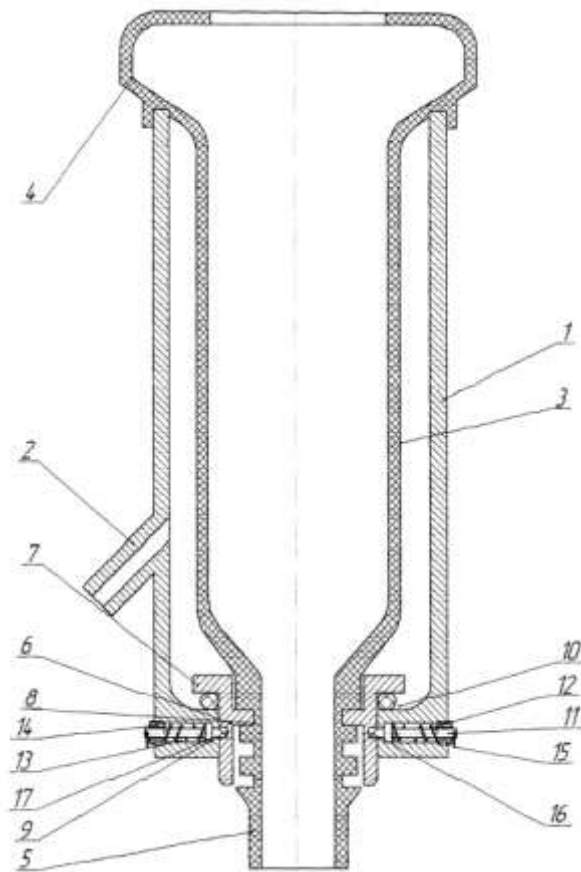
Доїльний стакан з фіксованим натягом дійкової гуми: 1 – корпус; 2 – повітряний патрубок; 3 – дійкова гума; 4 – присосок; 5 – молочна трубка; 6 – втулка; 7, 8 – верхній та нижній кільцеві бурти; 9 – кільцева виточка; 10 – прокладка кільцева; 11 – фіксатори; 12 – пружини; 13 – напрямні отвори; 14 – гвинти; 15 – упори; 16 – зріз фіксатора; 17 – упор фіксатора
